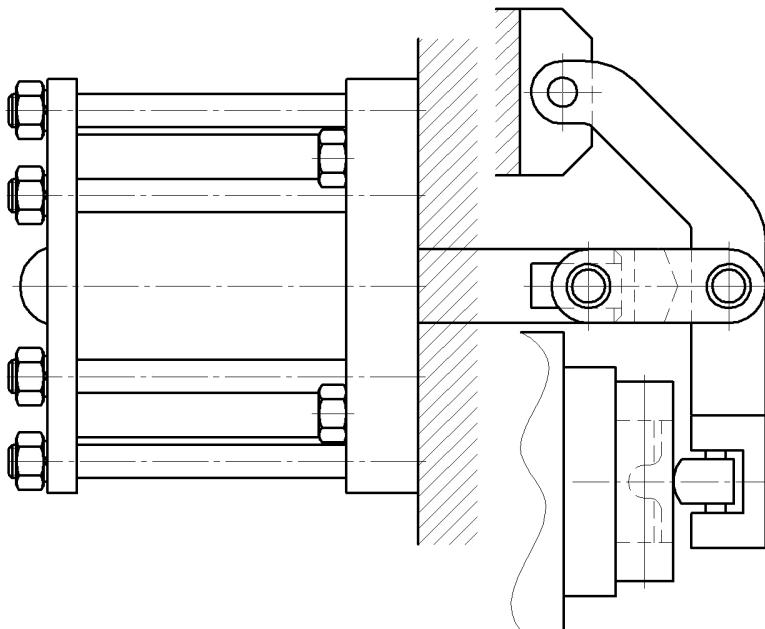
Эскиз расположения зажимного механизма и привода
